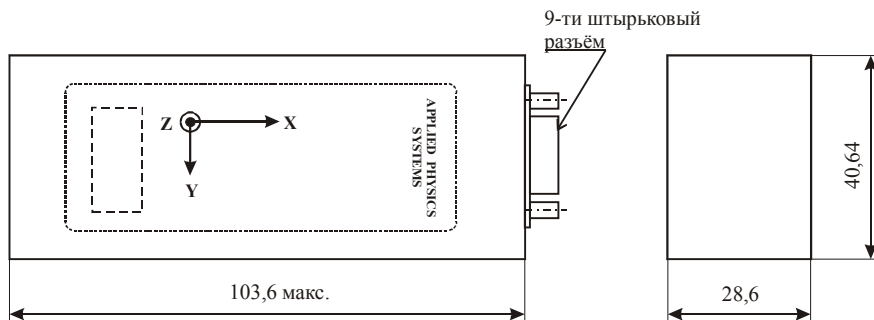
Внешний вид и габаритные размеры датчика типа APS-539
